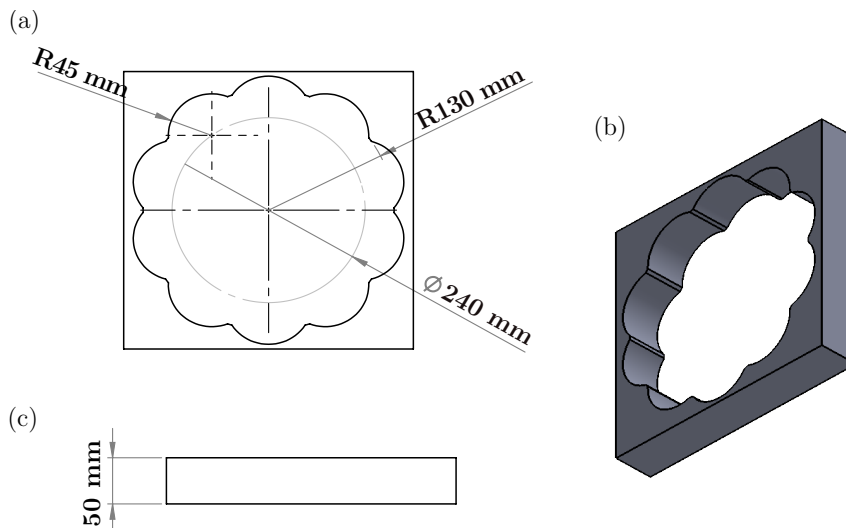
Schéma de la cuve fleurie. (a) - Vue du dessus. (b) - Vue 3D. (c) - Vue de côté.
